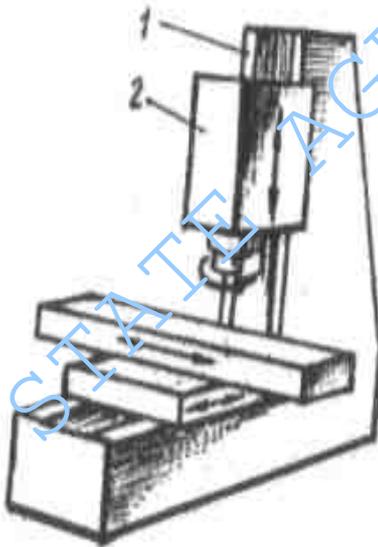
Вертикальный консольно-фрезерный станок
